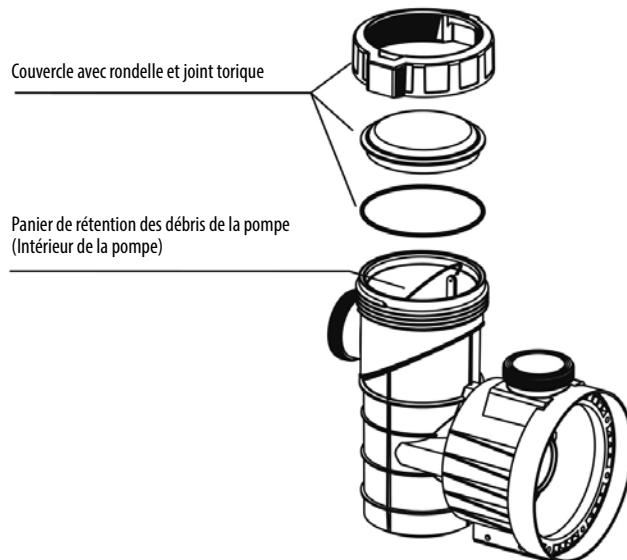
VUE ÉCLATÉE DE L'ENSEMBLE DU CORPS DE LA POMPE
